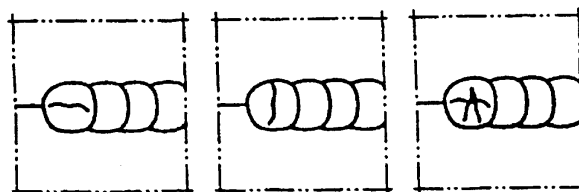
Кратерные трещины сварного соединения
